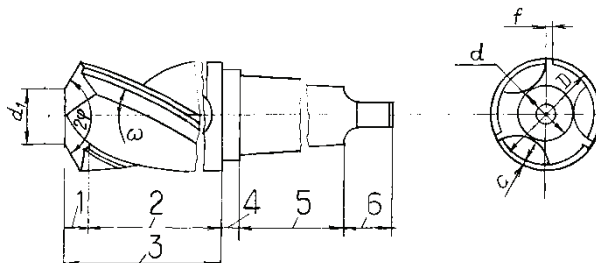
Конструктивные элементы цилиндрического хвостового зенкера
